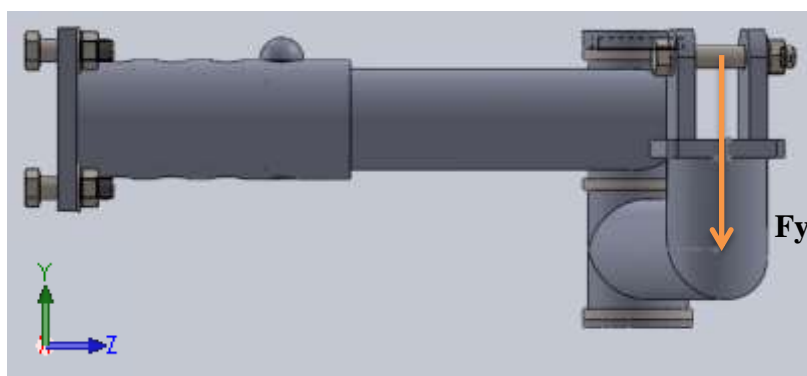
Esquema de cargas para la estructura soporte a 10 grados respecto alzado
